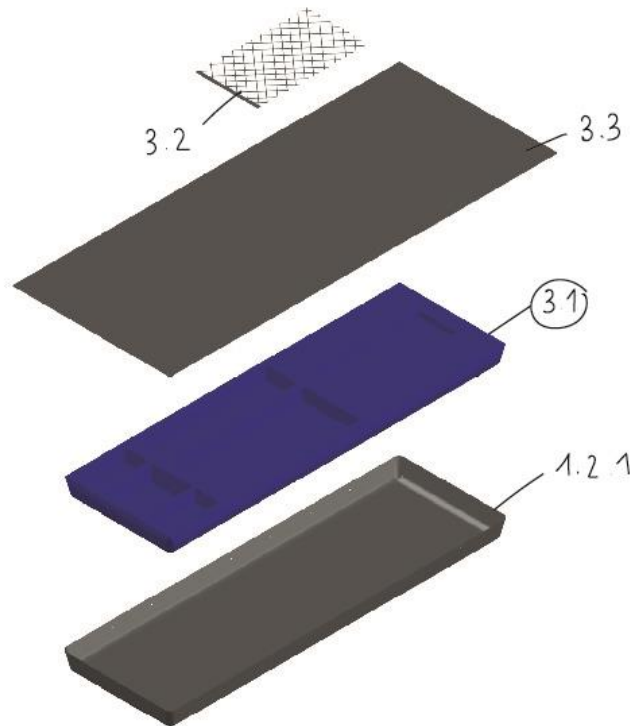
Explosionado de relaciones pieza 3.1
